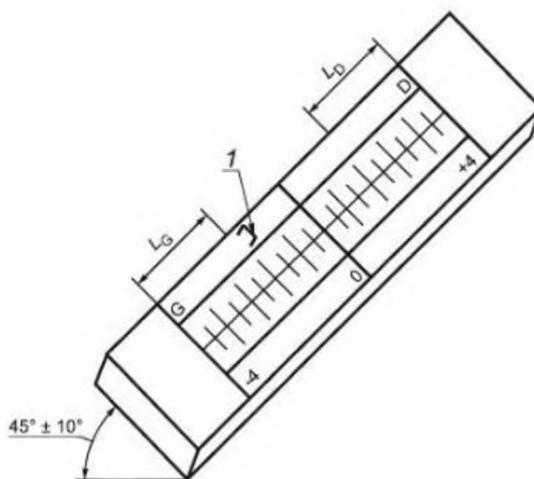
Стандартный контрольный образец типа № 1
